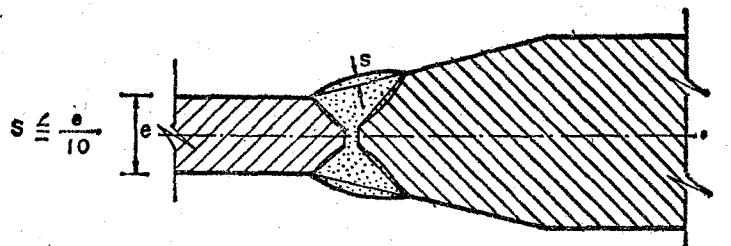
Sobreespesor  $s$  de una soldadura a tope
